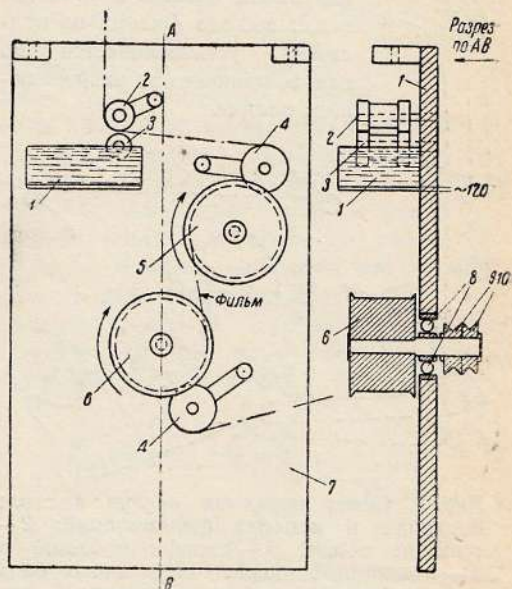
Схема устройства чистильно-парафинирующей приставки: 1 — ванночка с парафином; 2 — прижимной ролик; 3 — парафинирующий ролик; 4 — прижимной ролик; 5—6—чистильные барабаны; 7—корпус приставки; 8—шарикоподшипник; 9 — шкив пассика комбинированного барабана; 10 — шкив пассика автоматывателя
